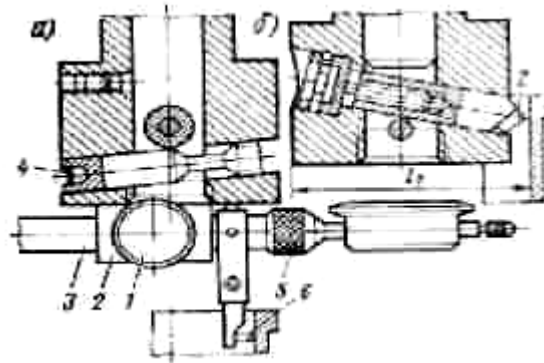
Різцева головка верстата 2А78Н з пристосуваннями для центрування гільз (а) і установки різця (б)
